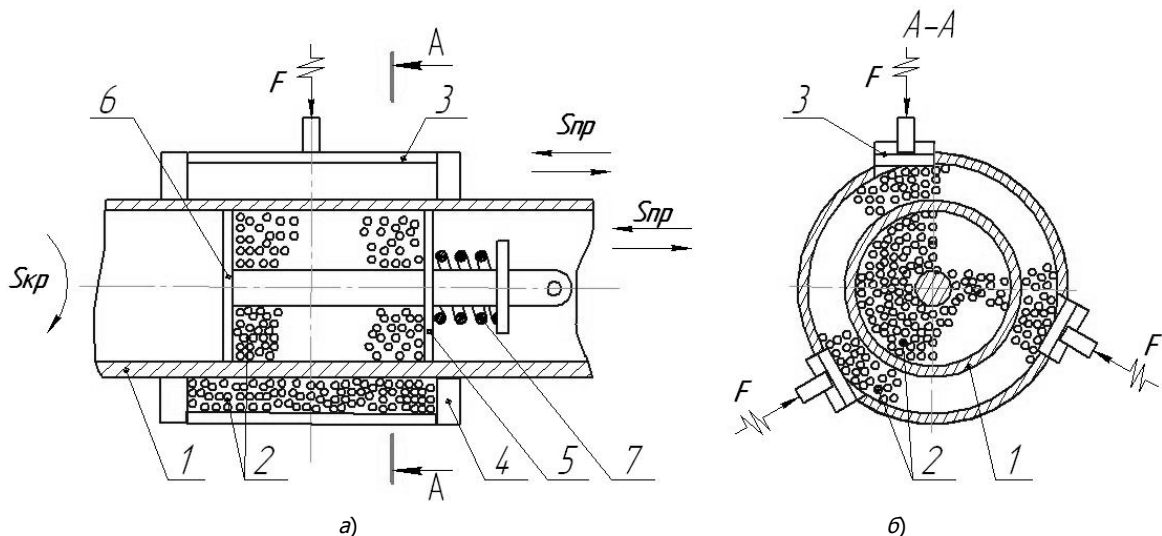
Приспособление, иллюстрирующее технологическую схему виброволновой обработки детали трубчатой формы: а — вид спереди, б — вид А-А для пояснения принципа работы; 1 — обрабатываемая деталь; 2 — среда стальных шаров; 3 — поджатие среды; 4 — корпус; 5, 6 — ограничители среды; 7 — пружина
